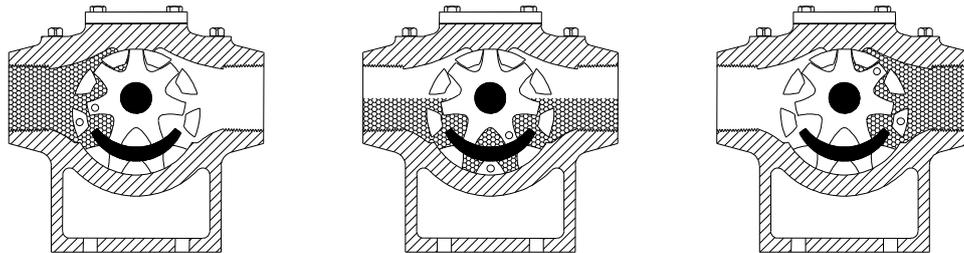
Flujo de líquido a través de la bomba ROTAN visto desde la parte delantera.
